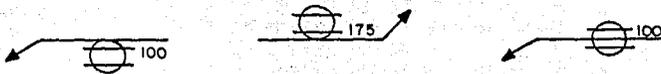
APLICACION DE DIMENSIONES A SIMBOLO DE SOLDADURA DE COSTURA
